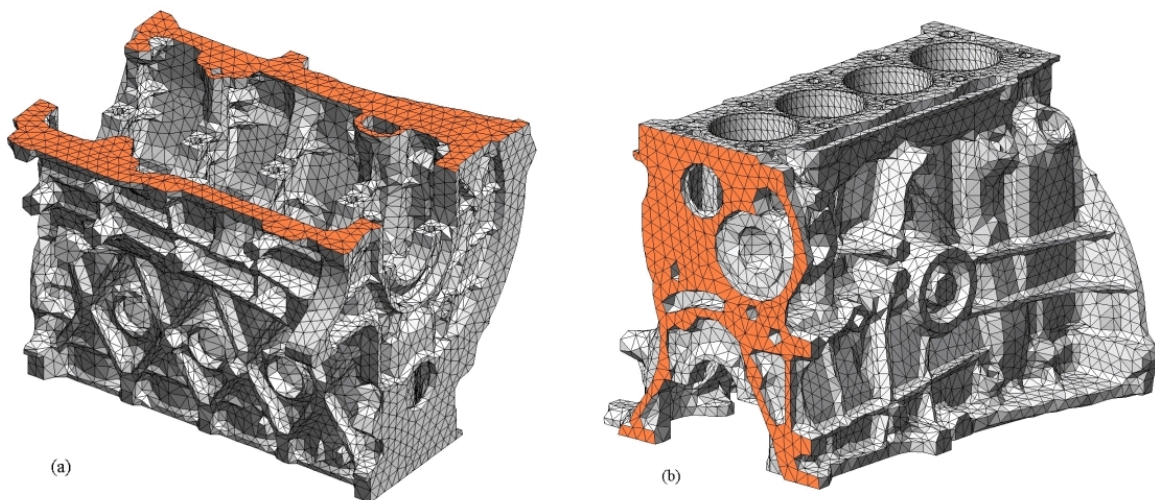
ébauche de la face 600 du carter-cylindres (a) et posage sur la face 600 pour usiner la face 300 (b)
